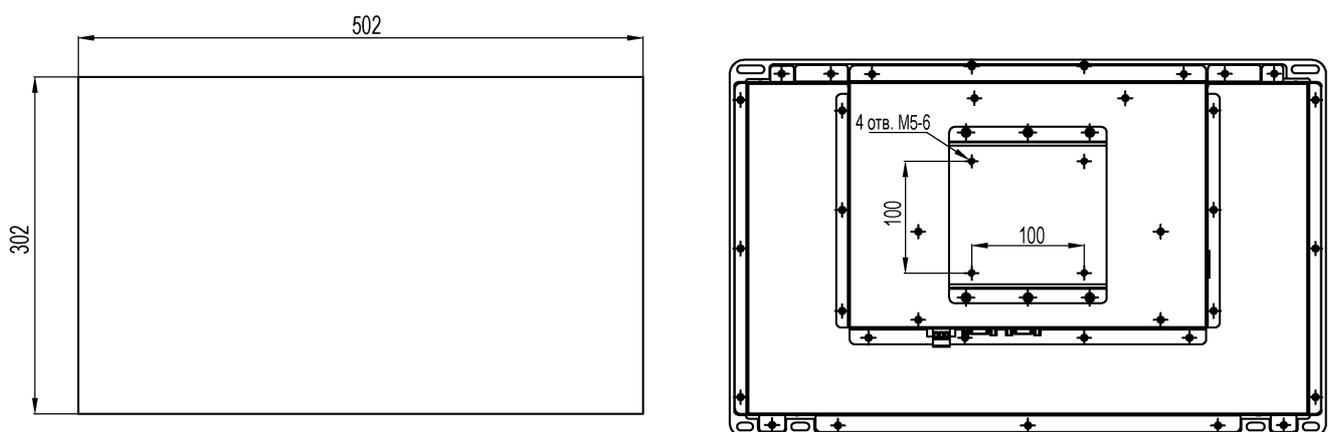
Габаритные и установочные размеры панели ETC-A8TS-HSSE-P-220
